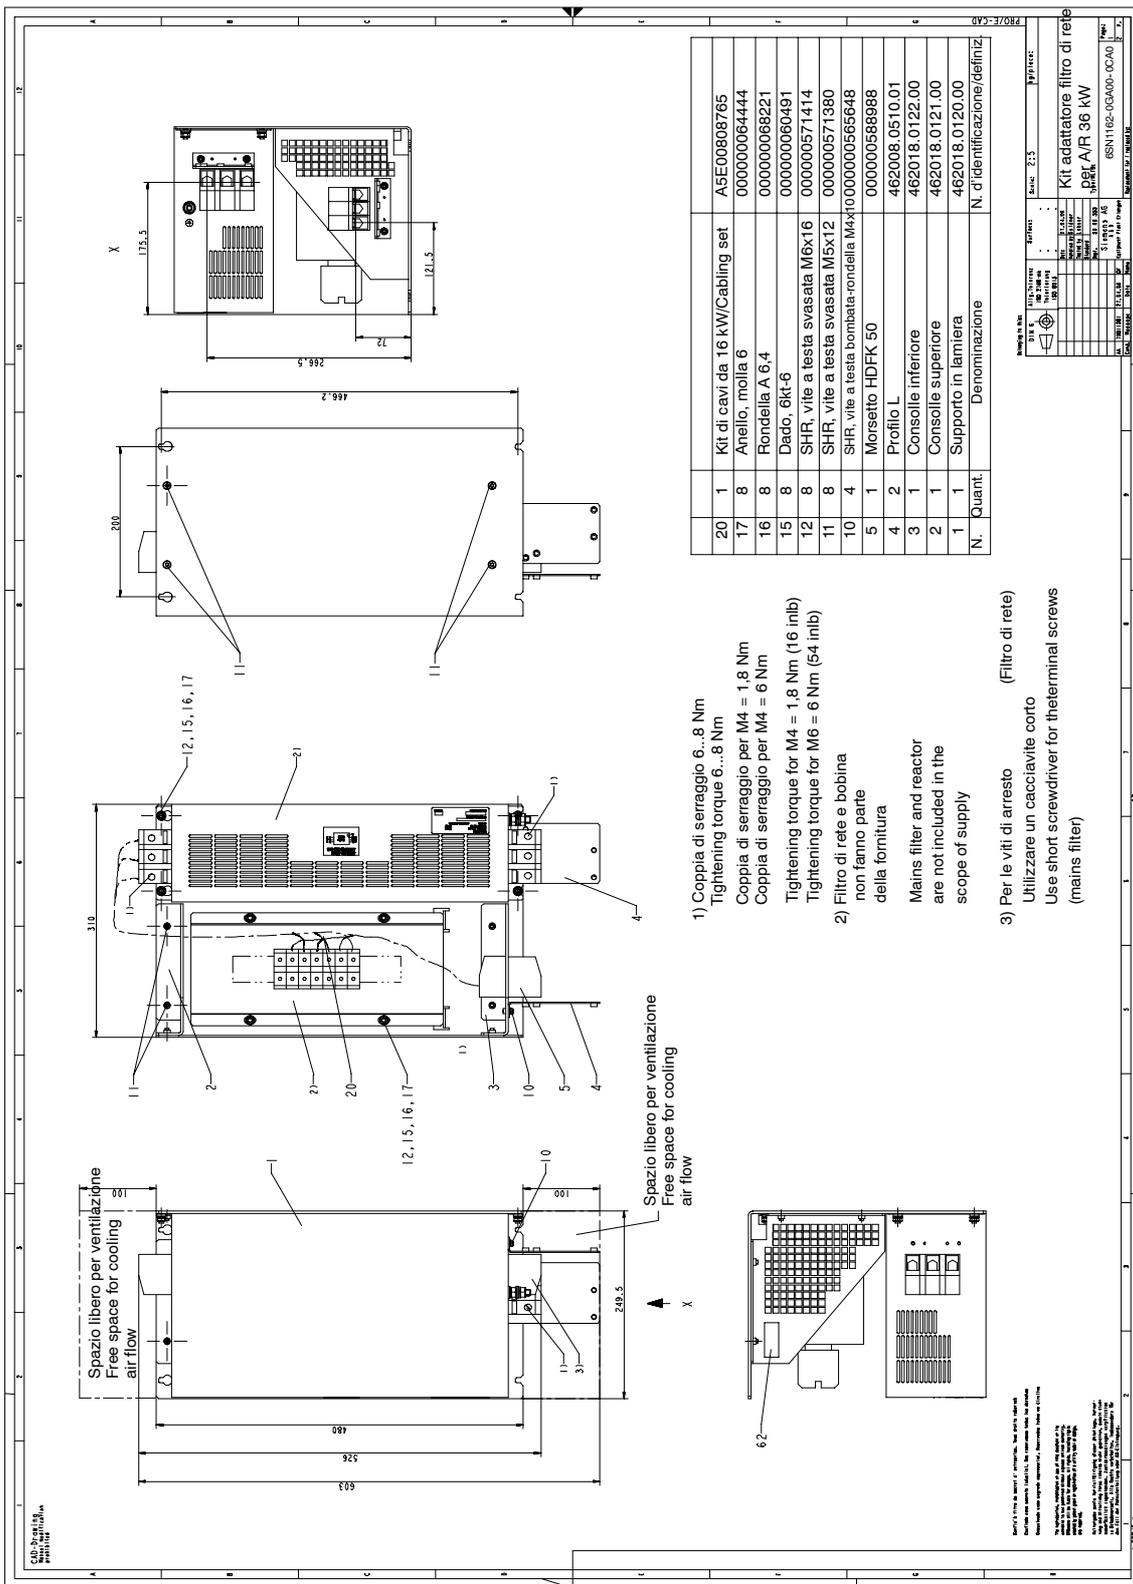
Kit adattatore filtro di rete per modulo E/R 36 kW, 6SN1162-0GA00-0CAx; disegno quotato
